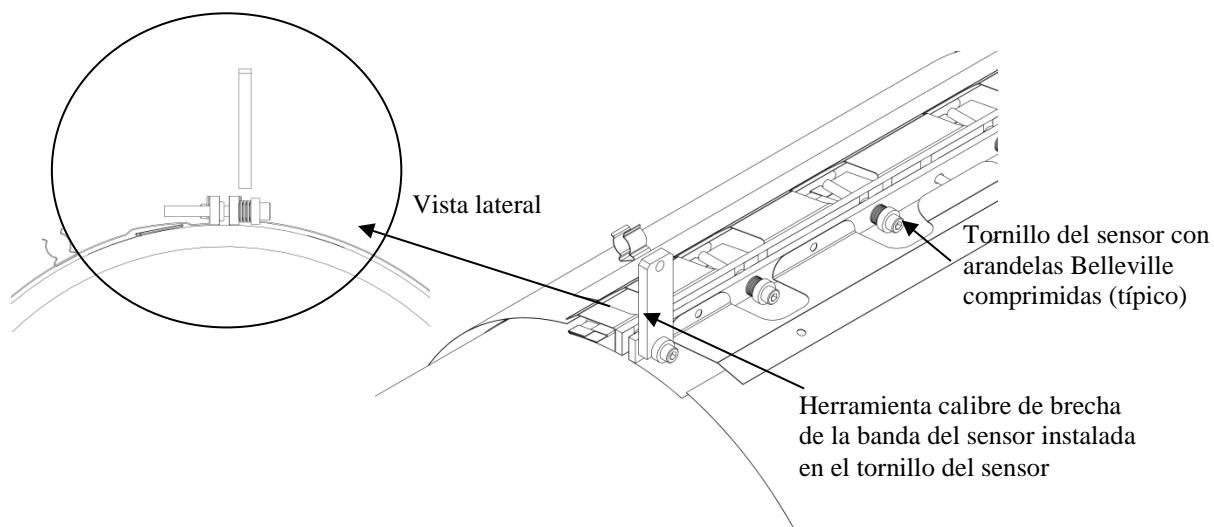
Herramienta calibre de brecha del sensor instalada en el tornillo del sensor
